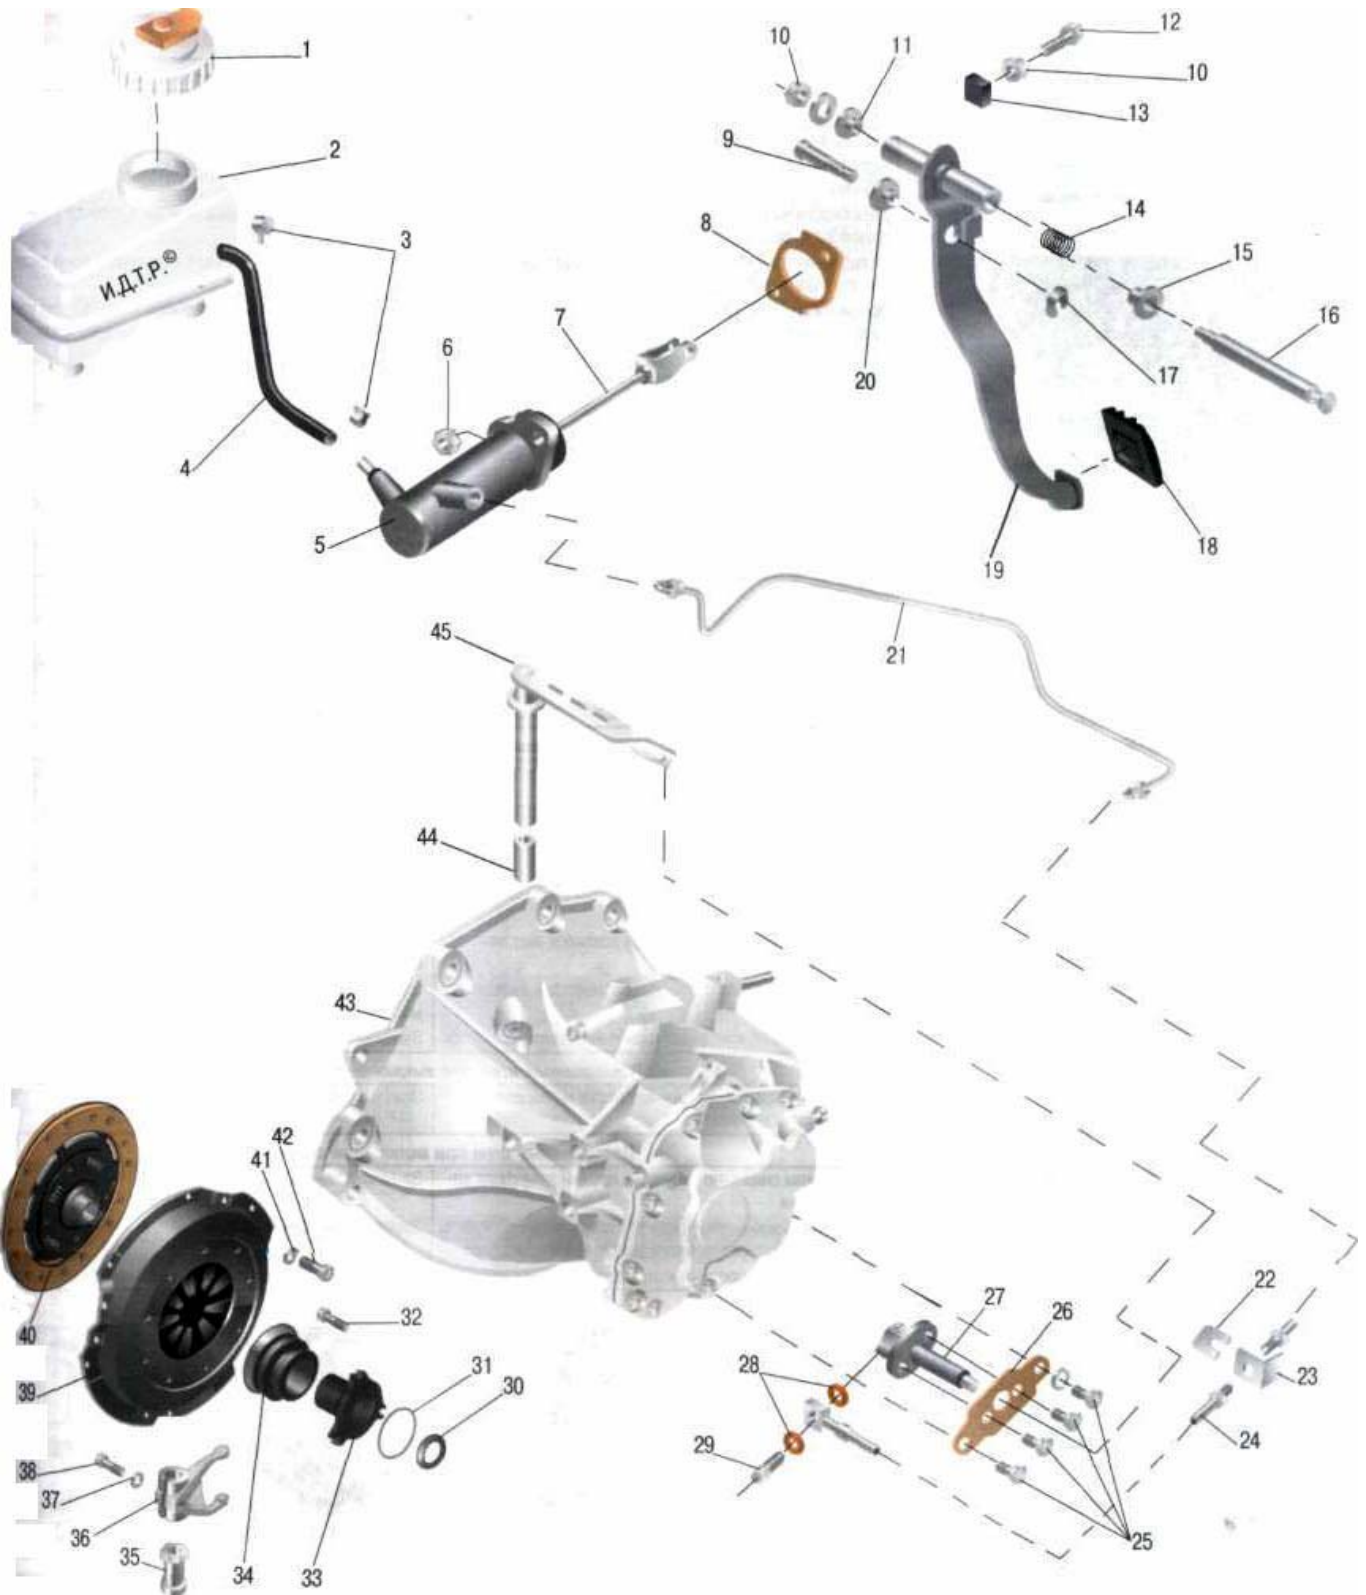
1. Сцепление и привод его выключения: 1 - пробка бачка гидроприводов тормозов и выключения сцепления; 2 - бачок гидроприводов тормозов и выключения сцепления; 3 - хомуты; 4 - шланг к главному цилиндру гидропривода выключения сцепления; 5 - главный цилиндр гидропривода выключения сцепления; 6, 10 - гайки; 7 - толкатель главного цилиндра гидропривода выключения сцепления; 8 - прокладка главного цилиндра гидропривода выключения сцепления; 9 - палец вилки толкателя главного цилиндра гидропривода выключения сцепления; 11, 15 - втулки оси педали сцепления; (2 - регулировочный болт; 13 - упор регулировочного болта; 14 - возвратная пружина педали сцепления; 16 - ось педали сцепления; 17 - стопорная шайба пальца вилки толкателя главного цилиндра гидропривода выключения сцепления; 18 - накладка площадки педали сцепления; 19 - педаль сцепления; 20 - волнистая пружинная шайба; 21 трубка гидропривода выключения сцепления; 22 - фиксирующая скоба шланга гидропривода выключения сцепления; 23 - кронштейн крепления шланга гидропривода выключения сцепления; 24 - шланг гидропривода выключения сцепления; 25, 32, 38, 32— болты; 26 - кронштейн крепления рабочего цилиндра гидропривода выключения сцепления; 27 - рабочий цилиндр гидропривода выключения сцепления; 28 - уплотнительные шайбы наконечника шланга гидропривода выключения сцепления; 29 - болт-штуцер крепления наконечника шланга гидропривода выключения сцепления; 30 - сальник первичного вала коробки передач; 31 - уплотнительное кольцо направляющей втулки подшипника выключения сцепления; 33 - направляющая втулка подшипника выключения сцепления; 34 - подшипник выключения сцепления; 35 - нижняя втулка вала рычага выключения сцепления; 36 - вилка выключения сцепления; 37, 41 - шайбы; 39 - кожух сцепления с нажимным диском; 40 - ведомый диск; 43 - картер сцепления; 44 - верхняя втулка вала рычага выключения сцепления; 45 - рычаг выключения сцепления.
